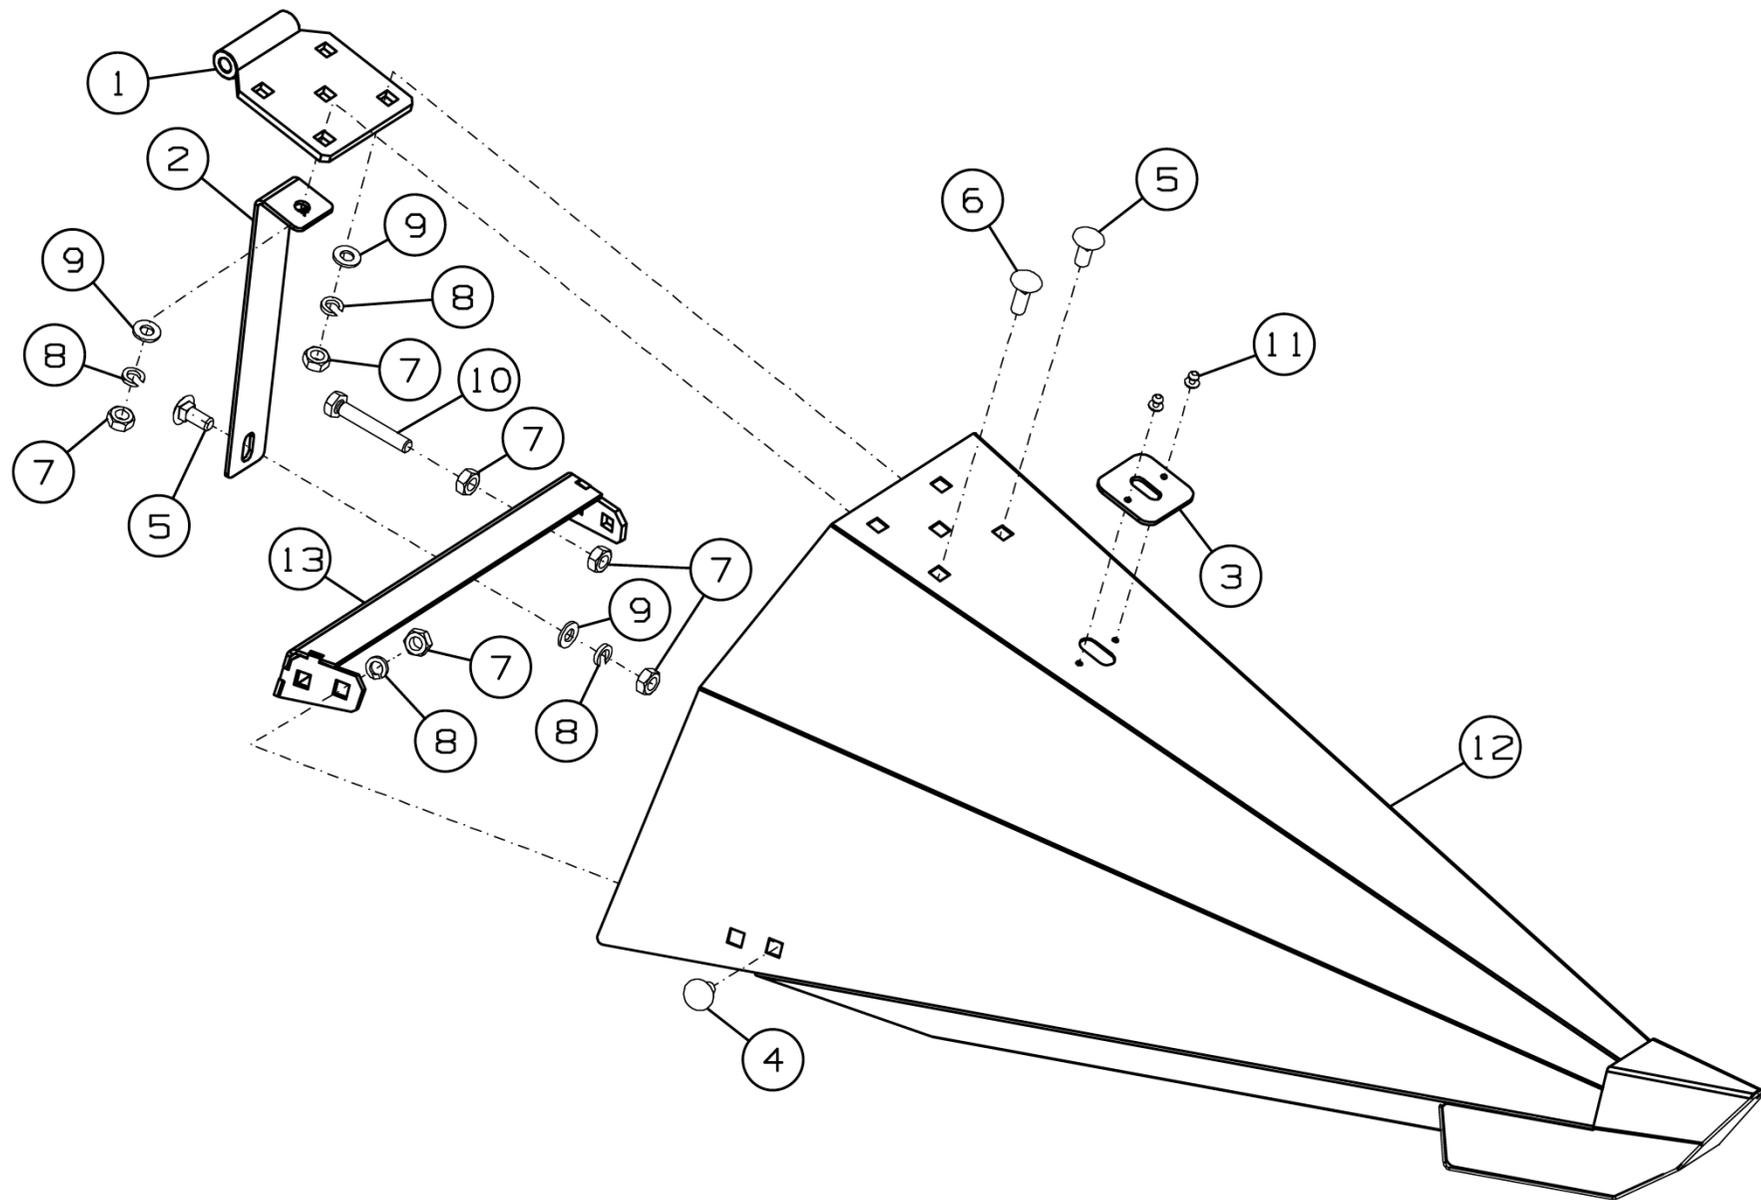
Делитель боковой ППК-870F.01.11.110
